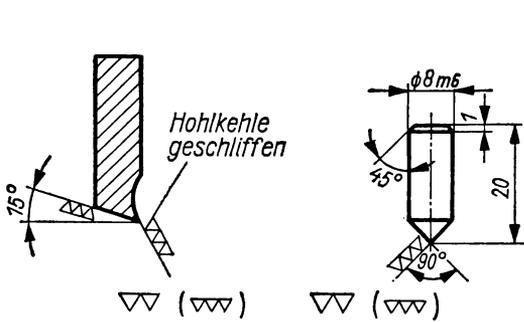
Teile für Schneid- und Stanzwerkzeuge mit dem Oberflächenzeichen „▽▽“
